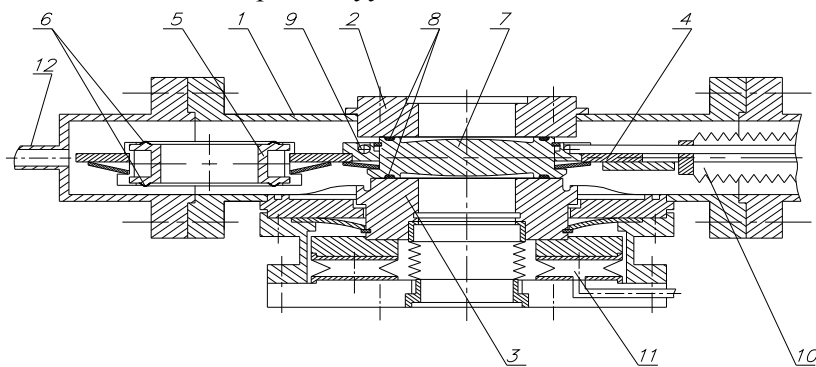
Конструкция сверхвысоковакуумного прогреваемого затвора:
